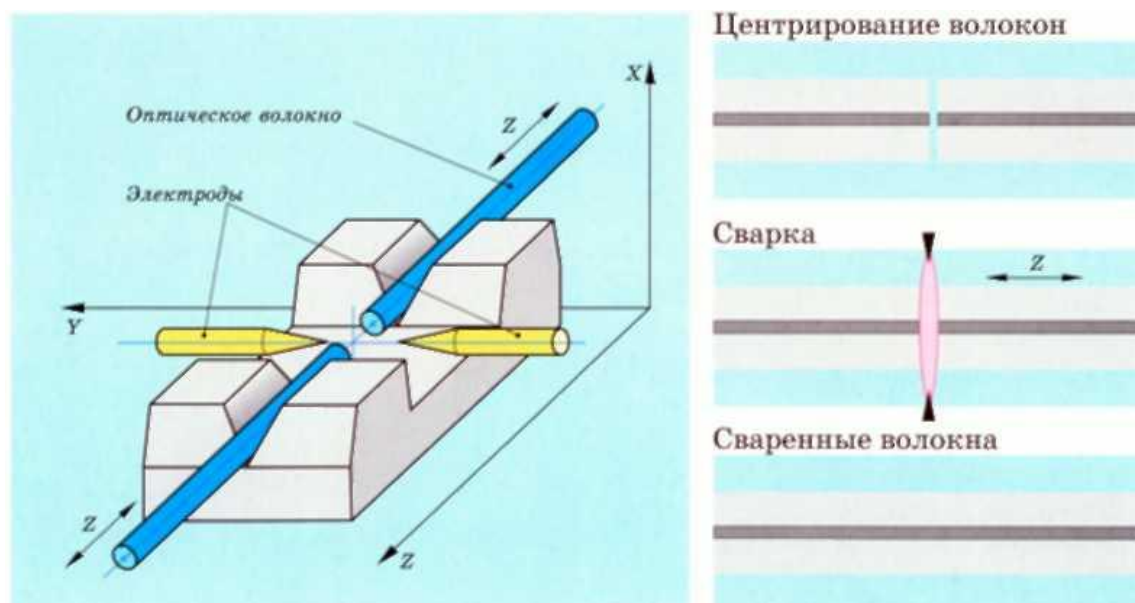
Принцип работы сварочного аппарата Fujikura FSM-18S
